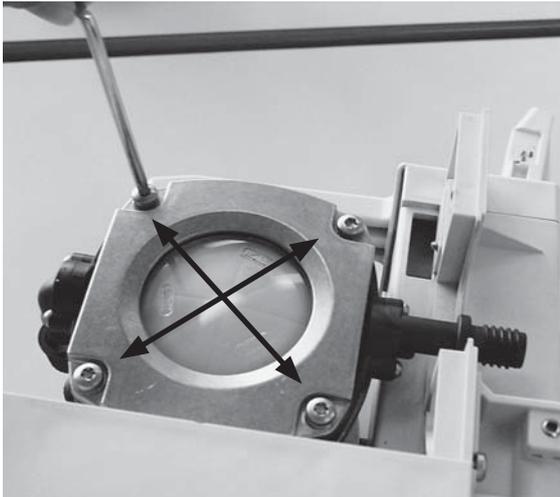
Désassemblage et réassemblage des têtes de soupape
